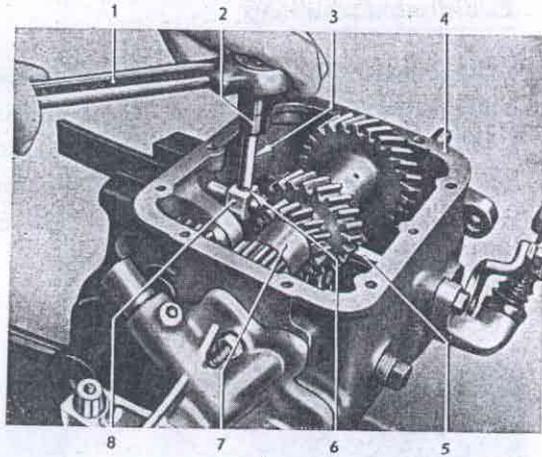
Sicherungsschraube aus Schaltzwischenhebel herausschrauben
